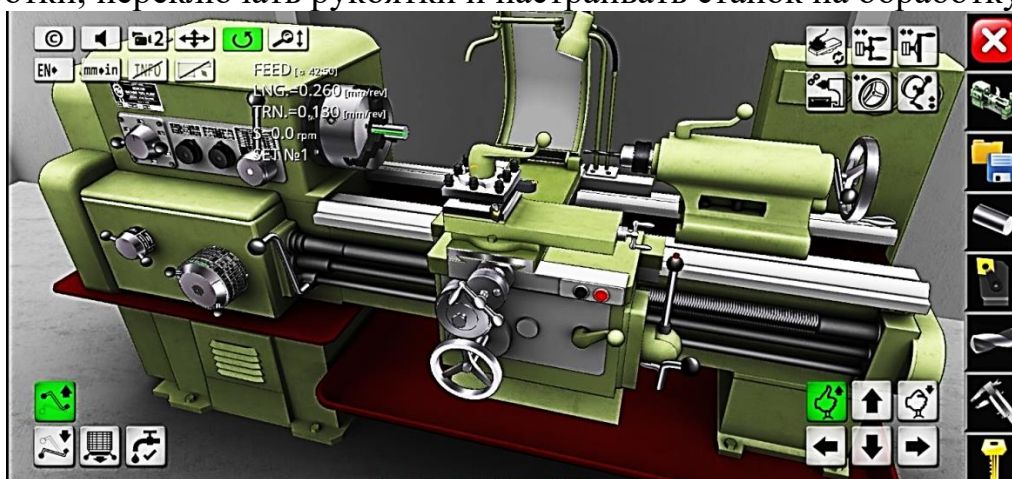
Симулятор токарного станка 1К62 LatheSimulatorLite
